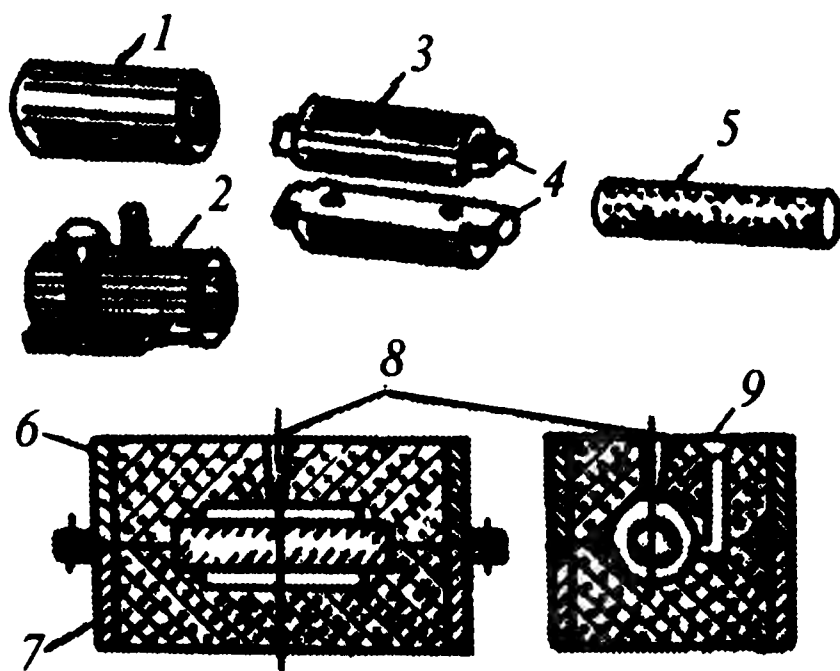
Деталь, отливка, элементы формовочного комплекта и песчаная форма:
